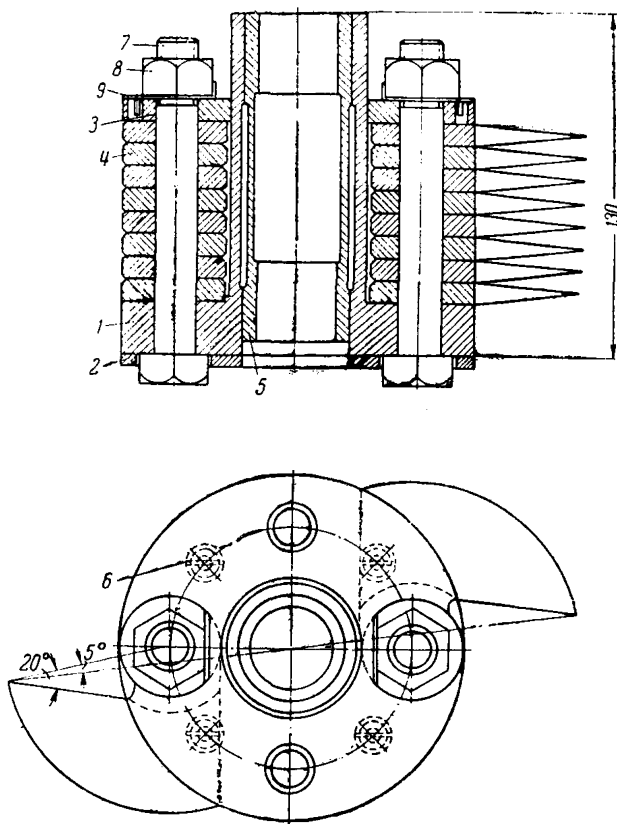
Конструкция фрезерной головки для нарезки стыков на зубчатый шип
